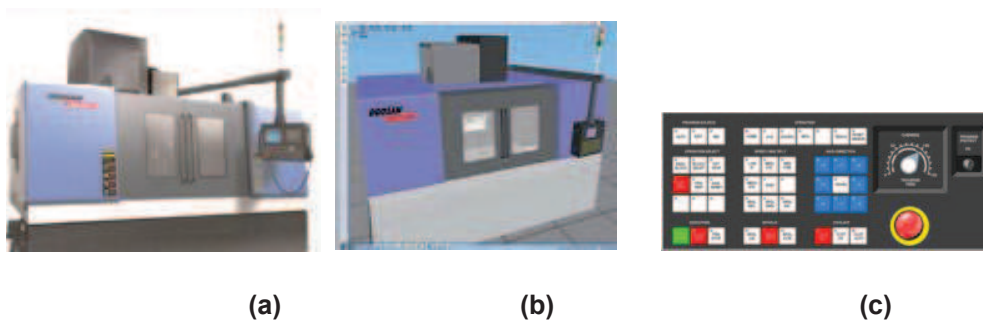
51. Centro de Mecanizado. (a) Máquina Real, (b) Máquina Virtual, (c) Controlador y panel CNC Virtual.
